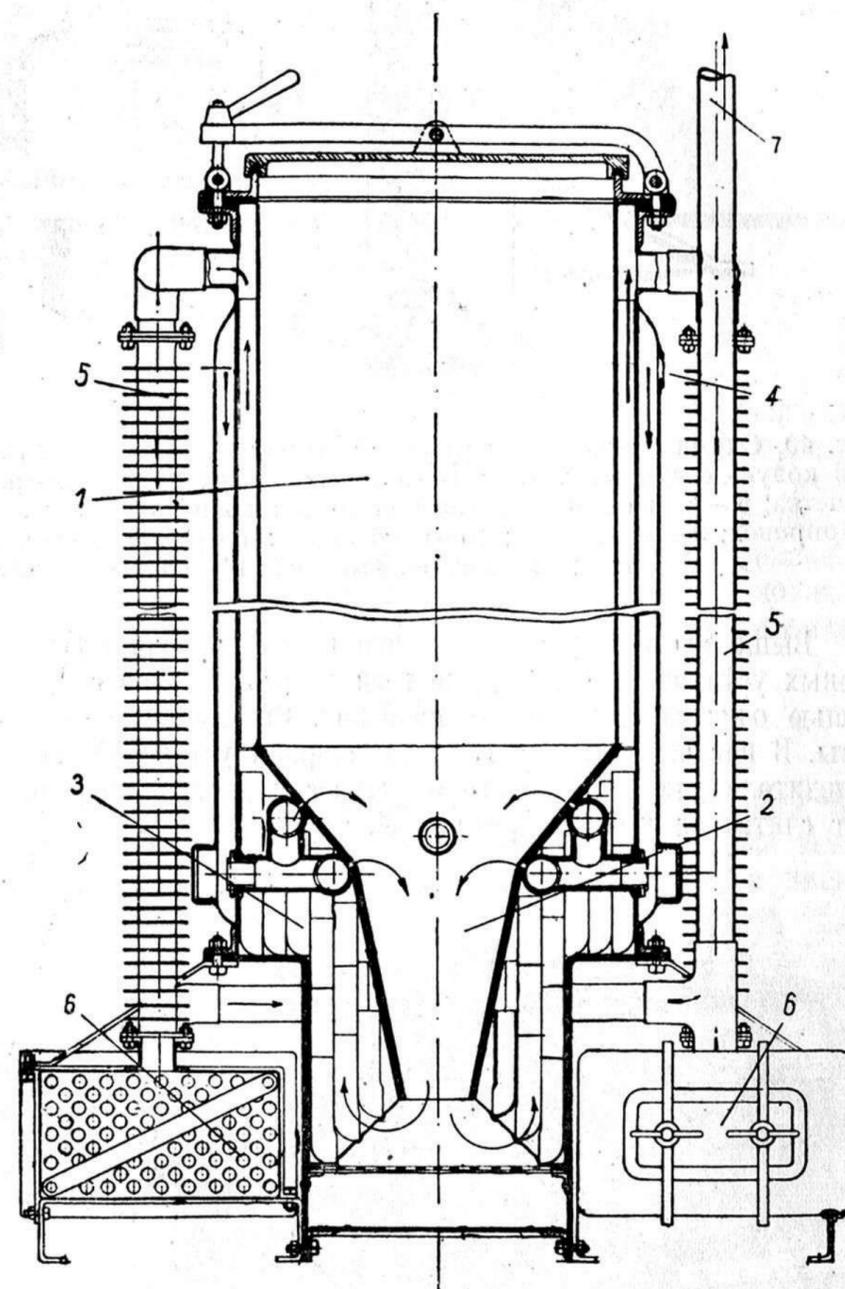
Газогенератор НАТИ-4. 1—шахта; 2—топливник; 3—катализаторы; 4—вход воздуха; 5—охладители газа; 6—очистители газа; 7—выход газа
